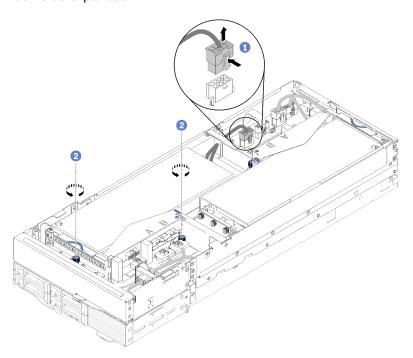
Desconectando o cabo de alimentação auxiliar e soltando os parafusos prisioneiros do conjunto de placa riser frontal
